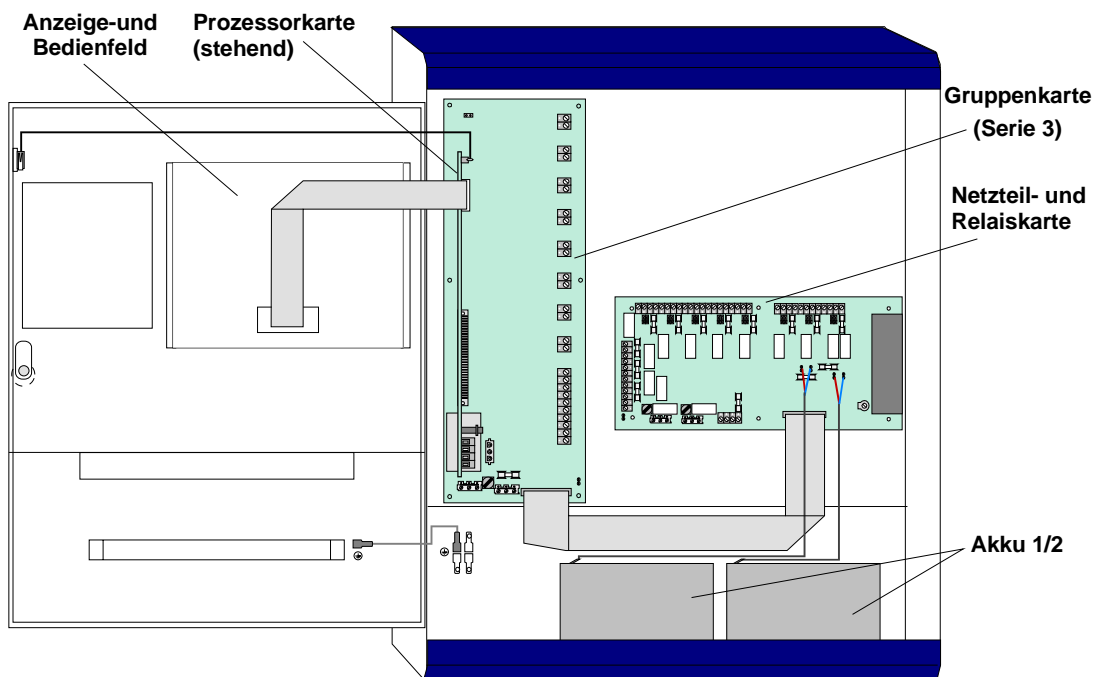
Geöffnetes Gehäuse / Lage der Baugruppen
